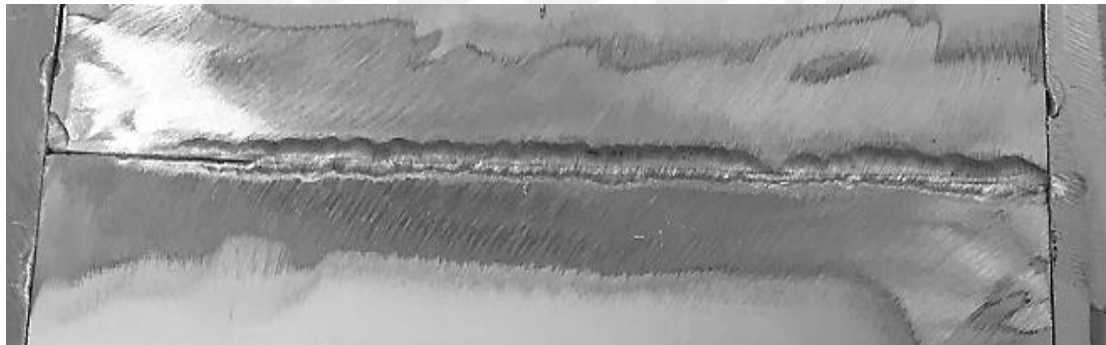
Penetración incompleta de una junta soldada sin material de aporte
